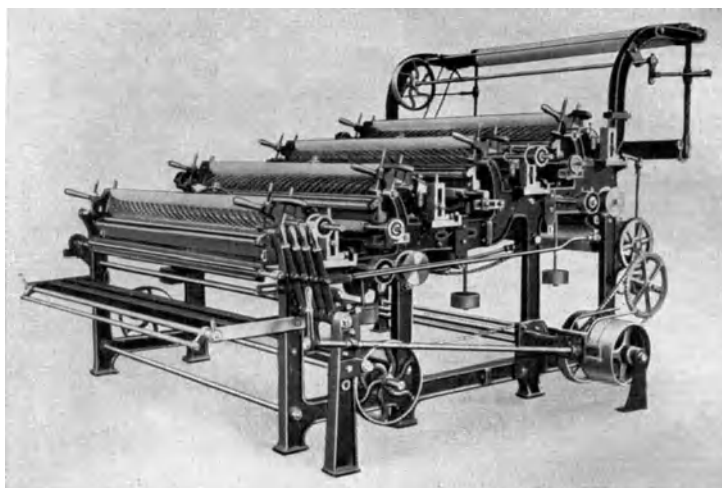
Vierzylinderschermaschine. (Sellers & Co., Huddersfield.)
